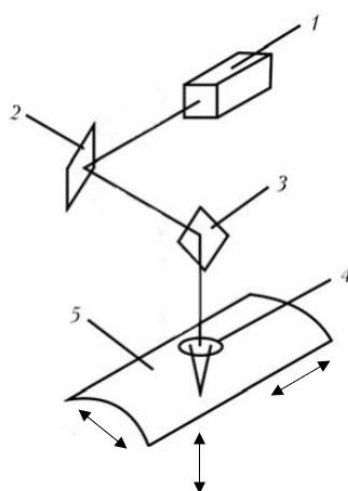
ЛТО для розмітки поверхні складної форми [32]
